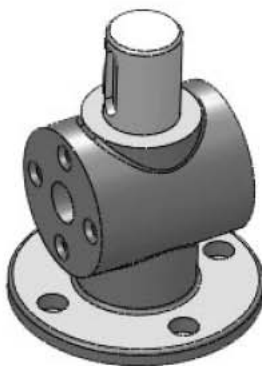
Подборка корпуса с пробкой и уплотнительными кольцами
